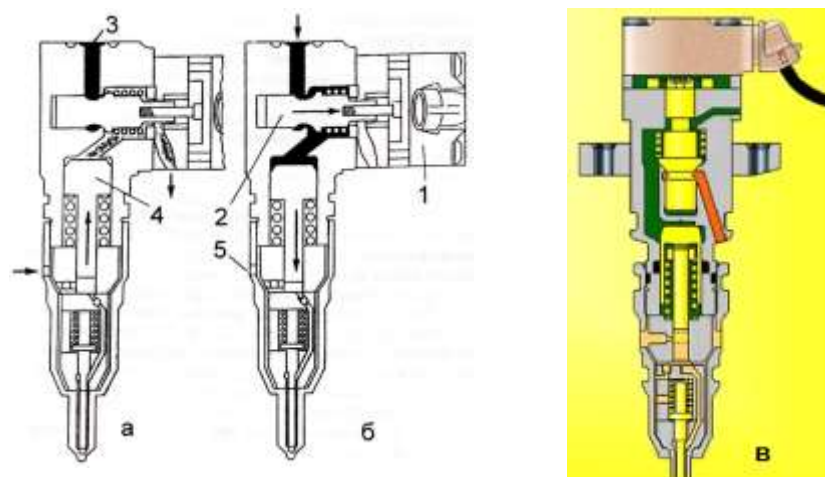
Конструктивная схема насос-форсунки HEUI: а - ожидание; б - впрыскивание; позиции рис. 1.132; в - более поздняя конструкция с осевым расположением клапана.
